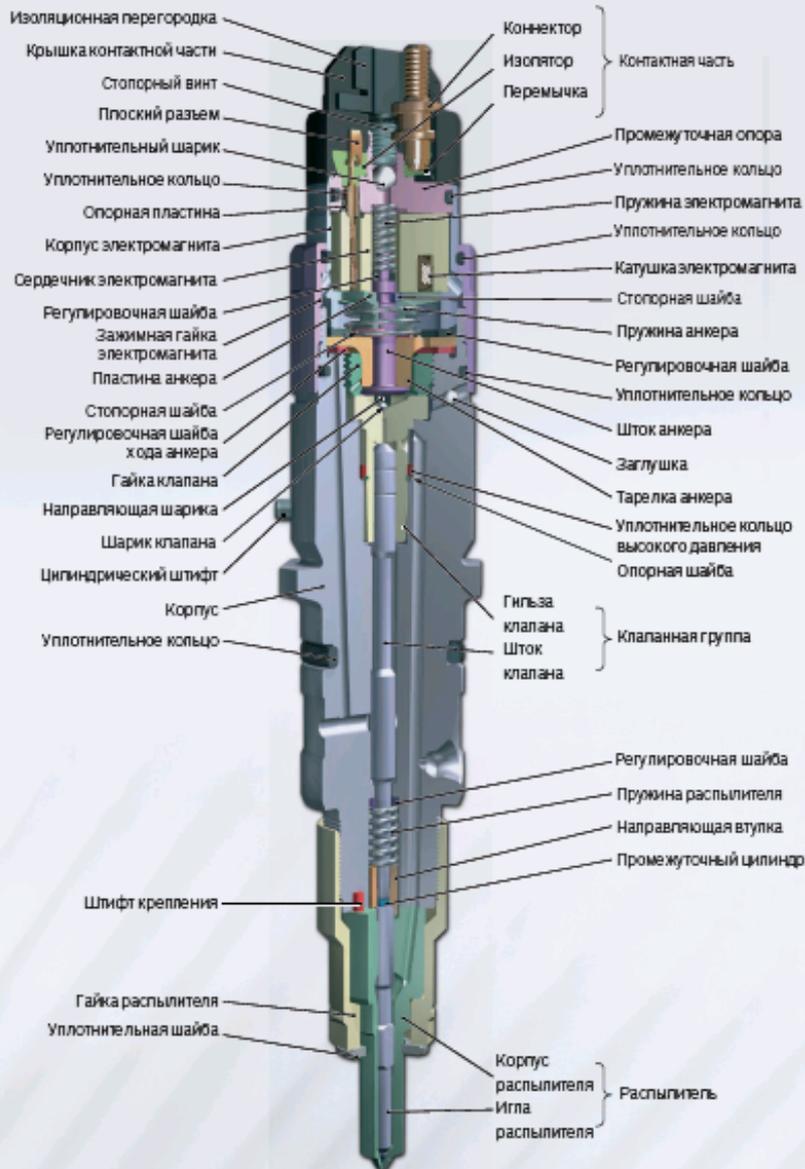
Форсунка Bosch CRIn1 для легковых автомобилей
